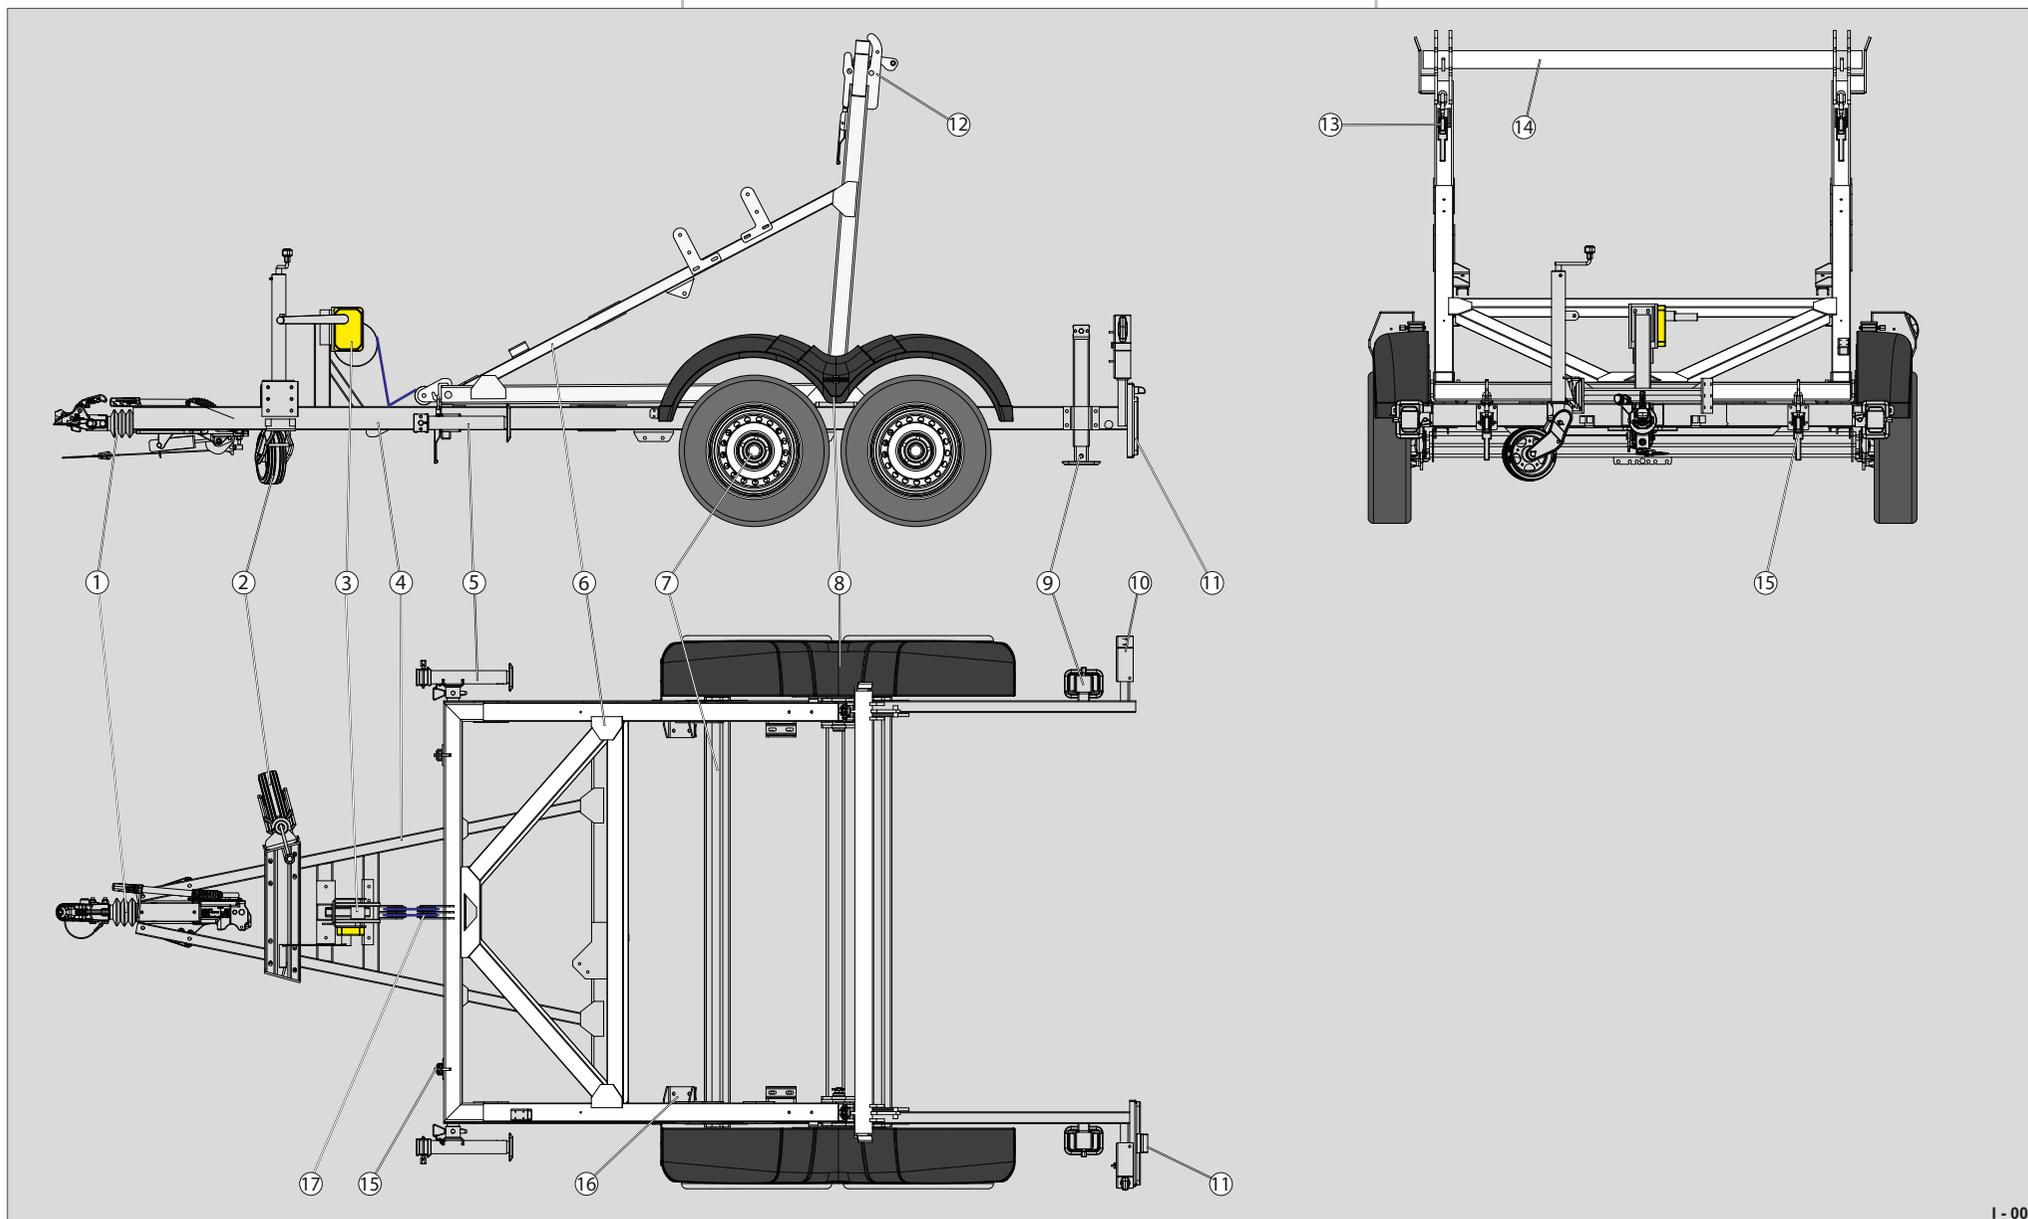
Vue d'ensemble de la remorque porte-touret (version standard)
